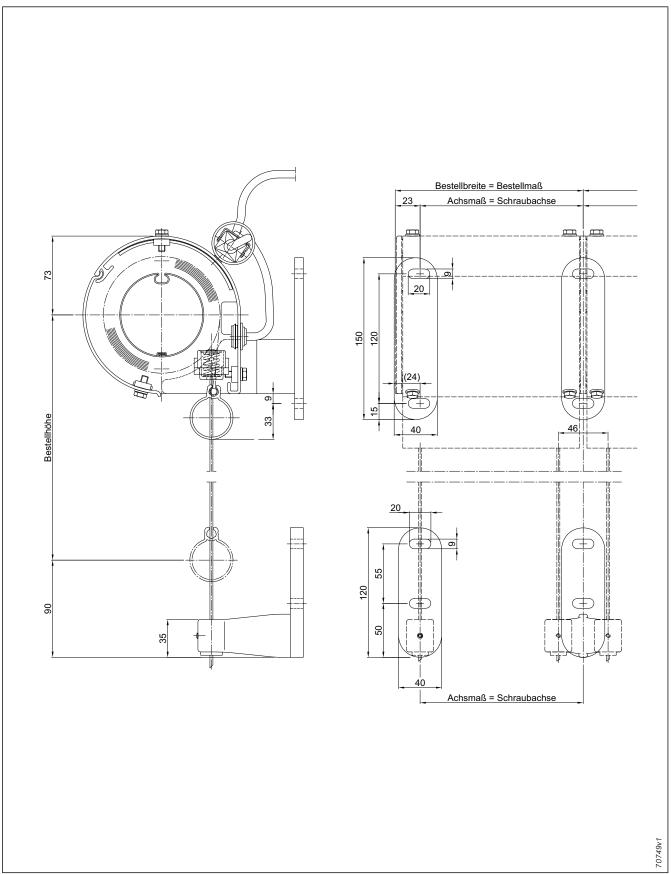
Fassaden-Markise 207 mit Rundblende Typ 8.3, Befestigungsmaße Gruppenanlage
